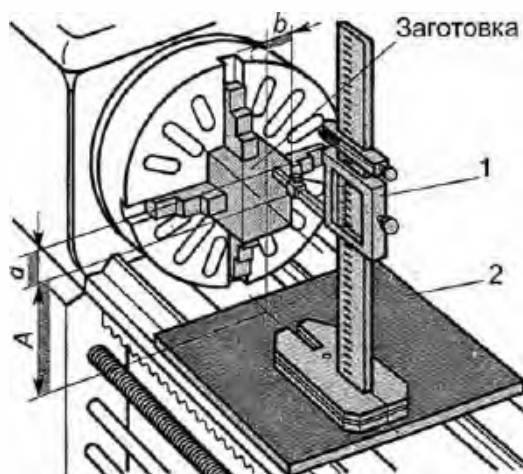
вивірення заготовки у чотири-КУЛАЧКОВОМУ ПАТРОНІ за допомогою ШТАНГЕНРЕЙСМУСА.
